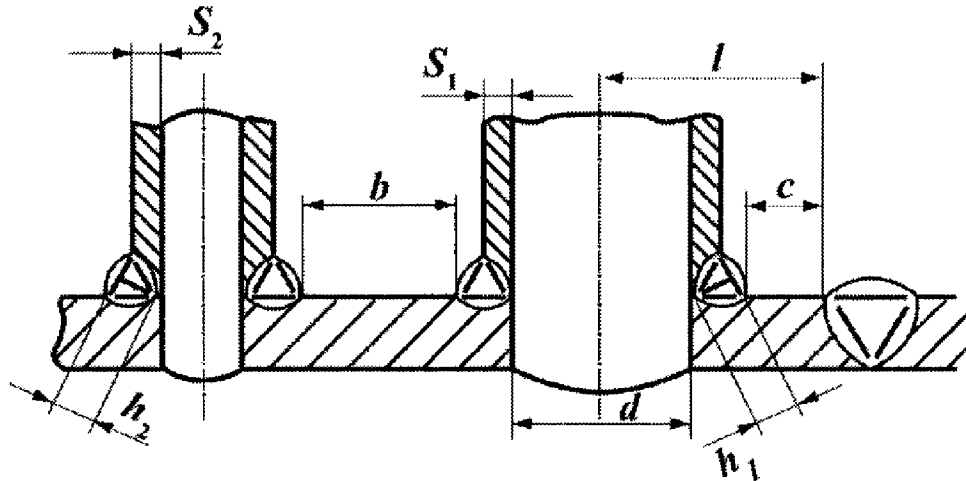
Розташування зварних з'єднань приварки патрубків:
